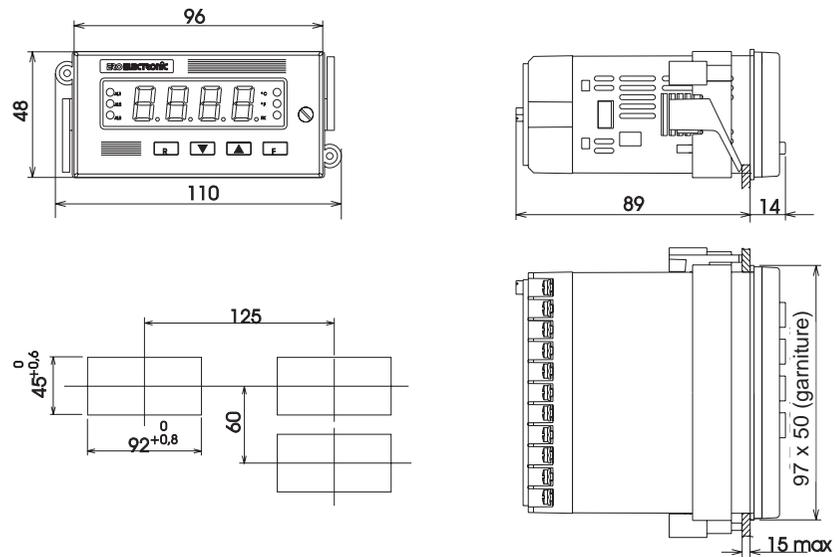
A TIS - DIMENSIONS ET PERCAGE
